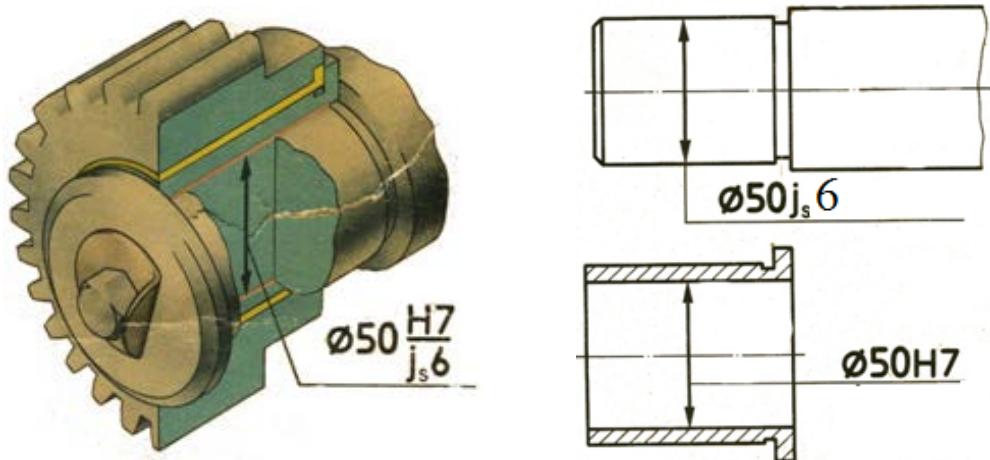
Втулка на конце вала редуктора (под вращающуюся на втулке шестерню)
